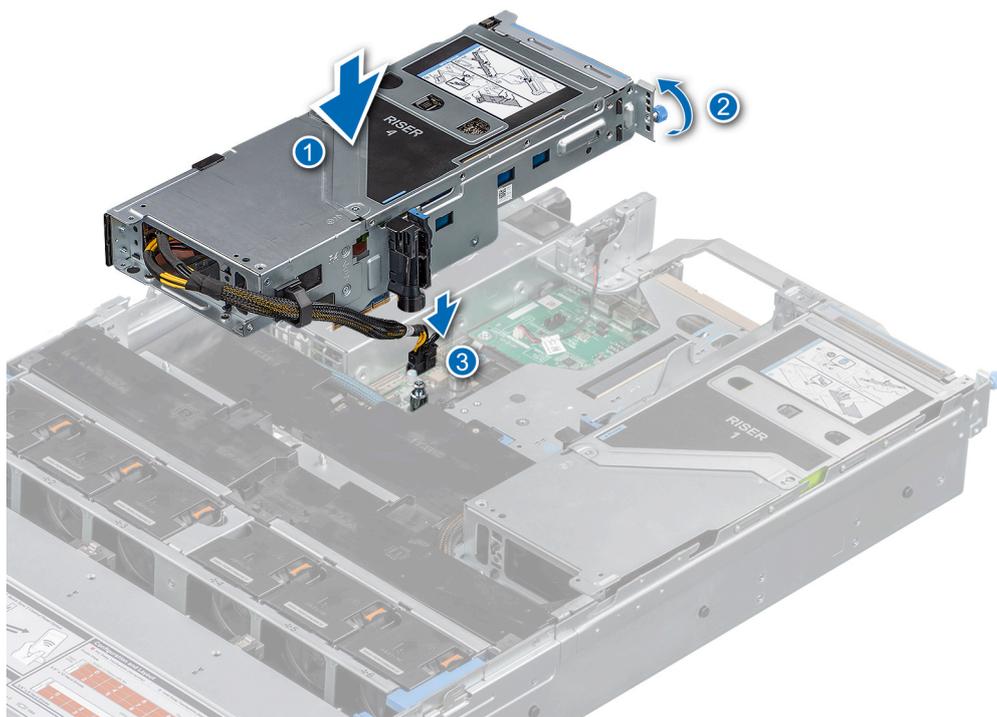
Installation de la carte de montage pour carte d'extension 4A
